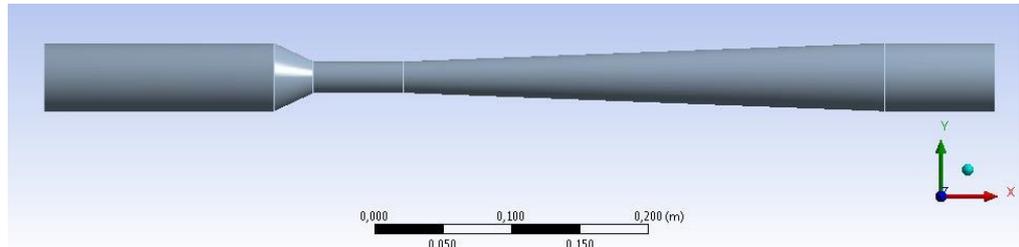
Venturi 3 - Comprimento da garganta 66 mm e Diâmetro da garganta 23 mm.
